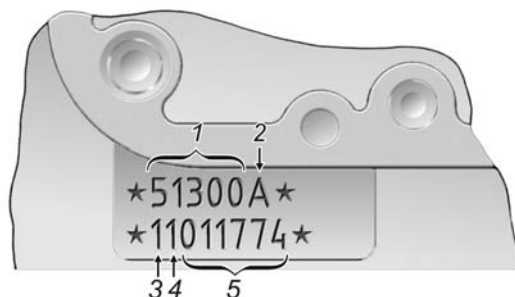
Пример нанесения номера двигателя ЗМЗ-5231:
